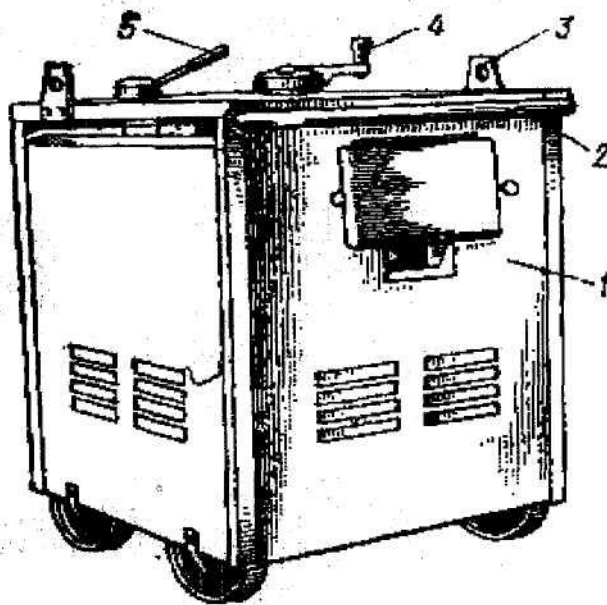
Сварочный трансформатор ТД-500:
